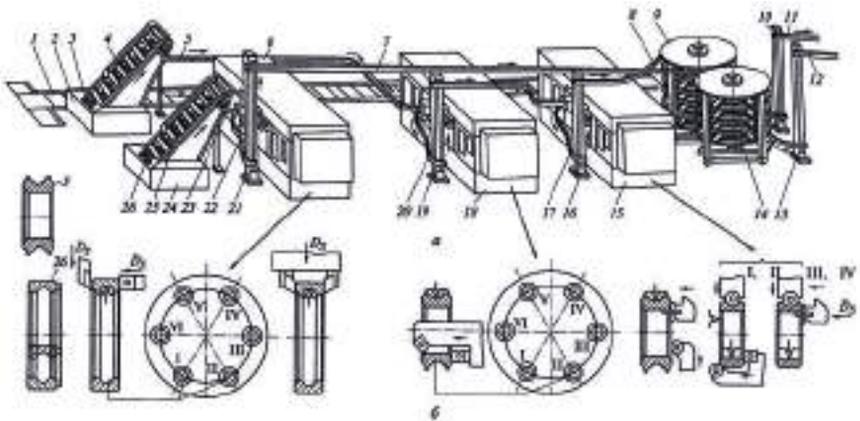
АЛ для токарной обработки колец шарикоподшипников:
